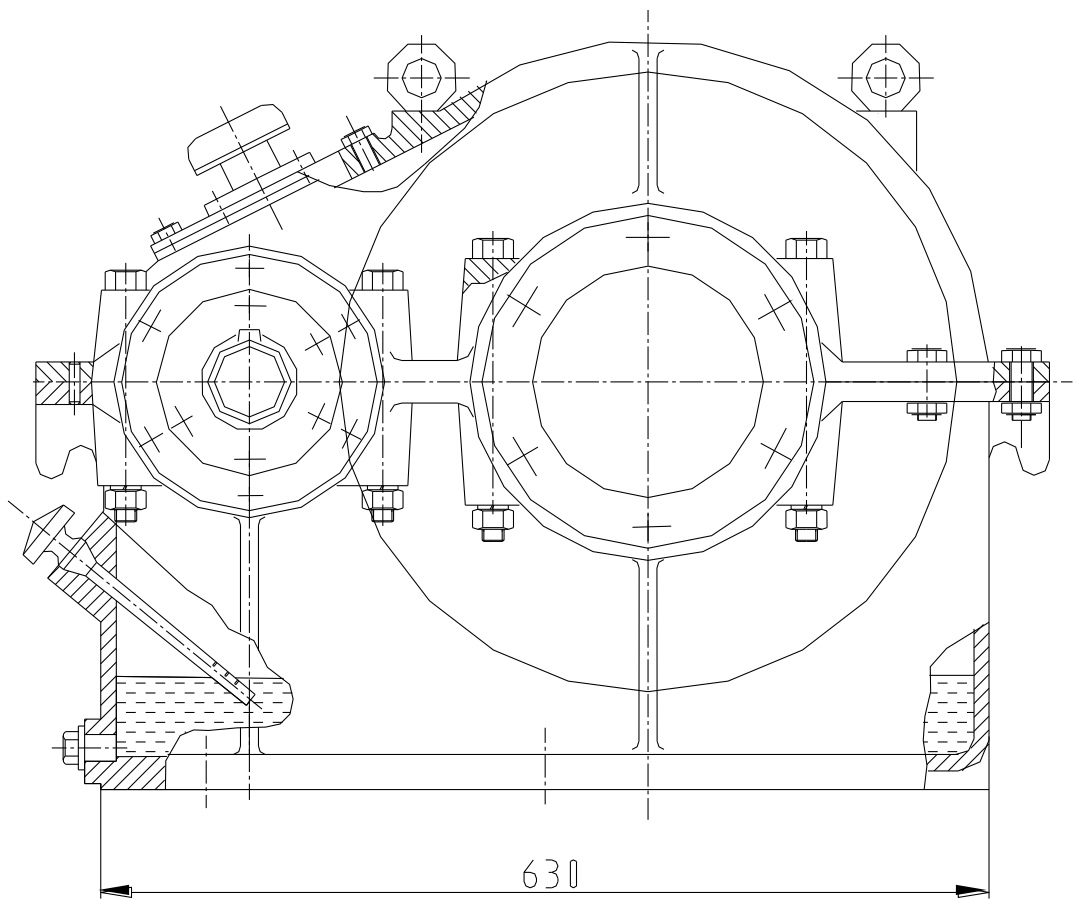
Редуктор циліндричний з Косозен убимі колесами
